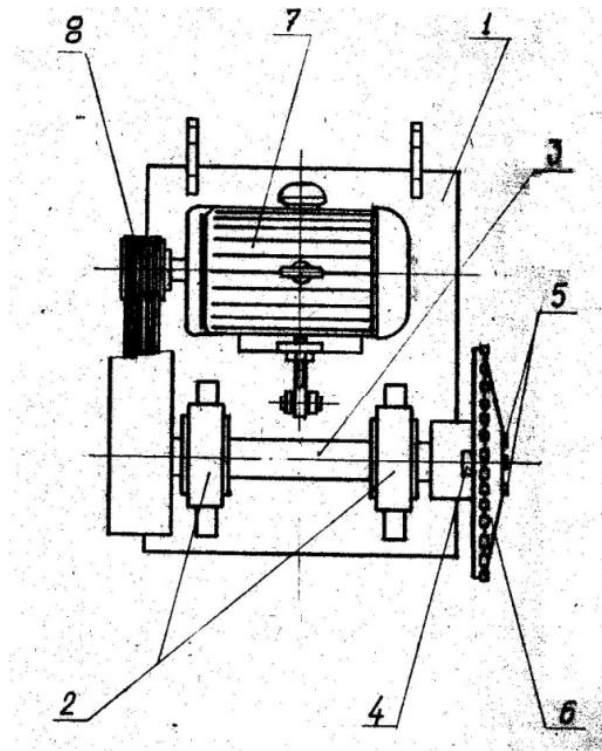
Принципова схема одношпindelного спеціального супорта до зубостругального верстата фірми «МАОГ»
